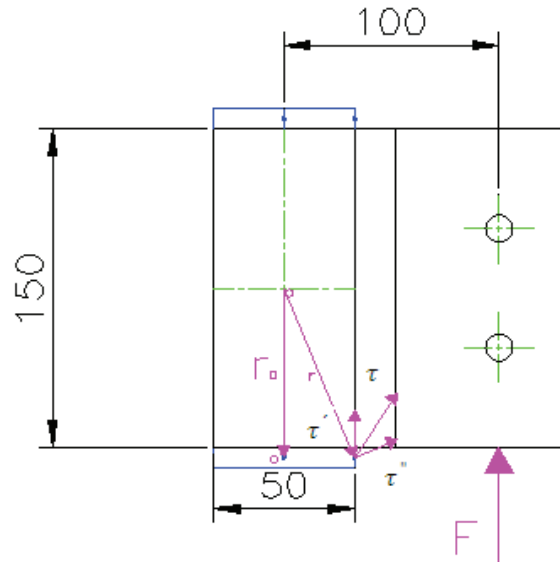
Diagrama de cuerpo libre de soldaduras.
